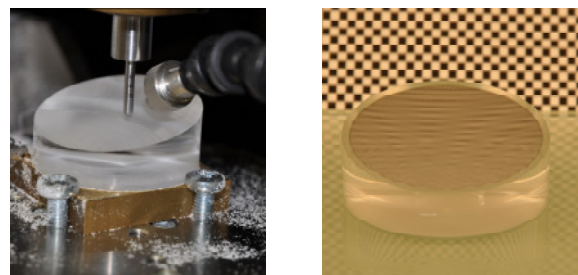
links: Fräsen der Freiformfläche mit monokristallinen Diamantwerkzeugen, rechts: Freiformfläche
